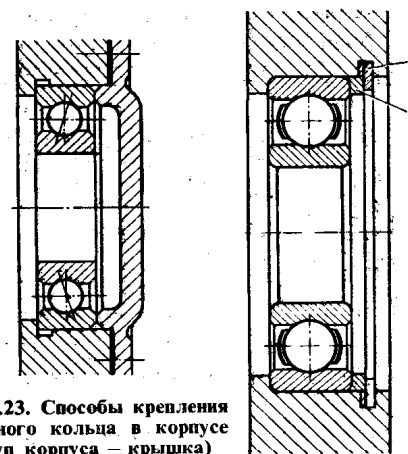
Способы крепления наружного кольца в корпусе (уступ корпуса — крышка)
